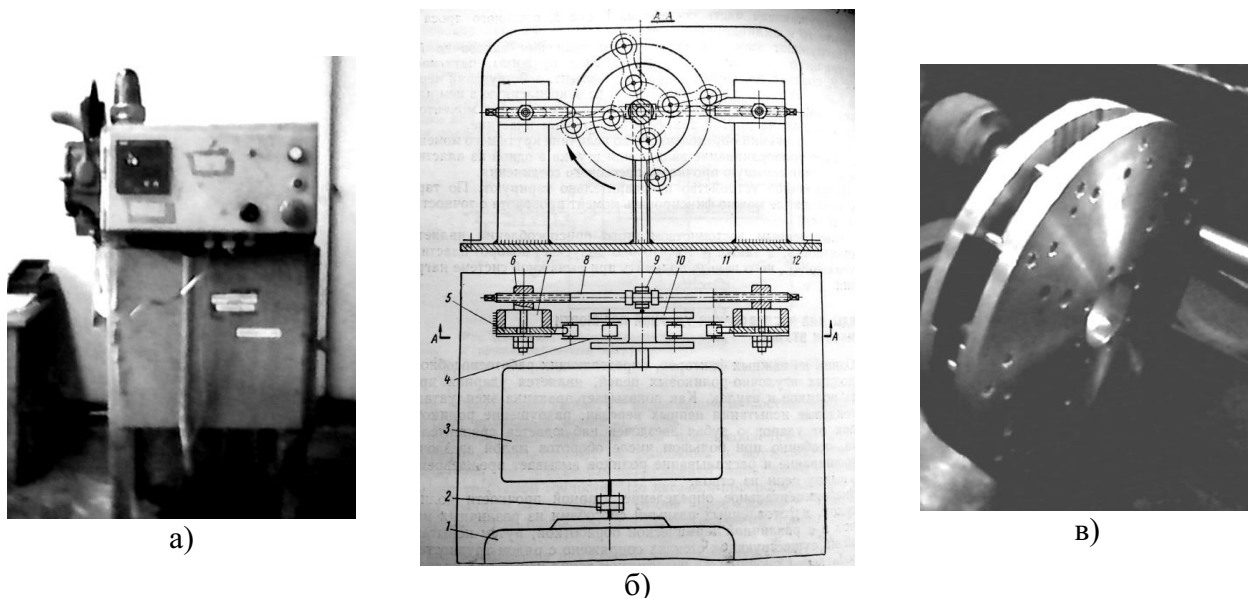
Стенд для испытания роликов на ударную прочность: а) внешний вид стенда; б) кинематическая схема стенда; в) внешний вид планшайбы
